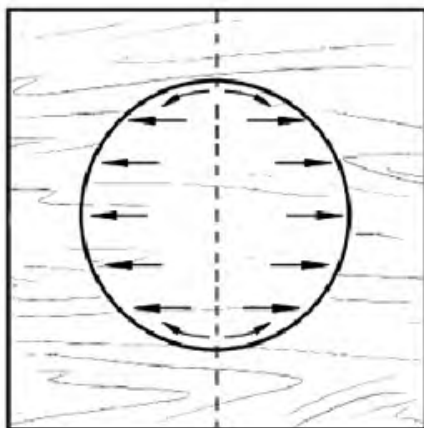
Выполнение круглой выпуклой формы на пласти заготовки вторым способом (стрелками указано направление движение инструмента)
